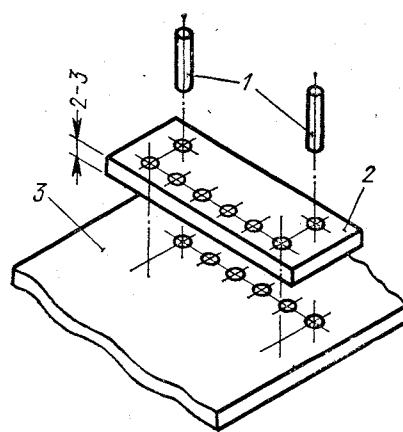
Приспособление для сверления рядов круглых отверстий: 1 — штифты; 2 — кондуктор; 3 — панель.
